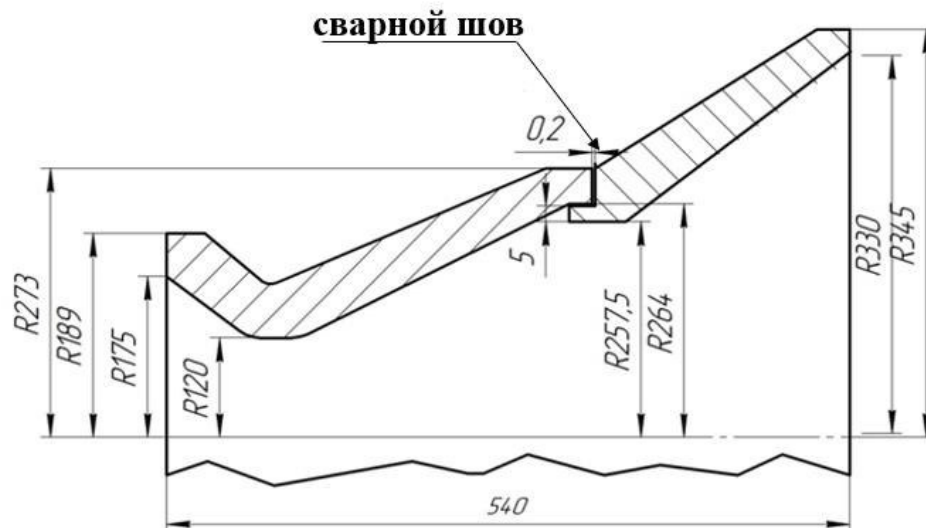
Эскиз сварного соединения стали 06X15H6MBФБ-Ш
